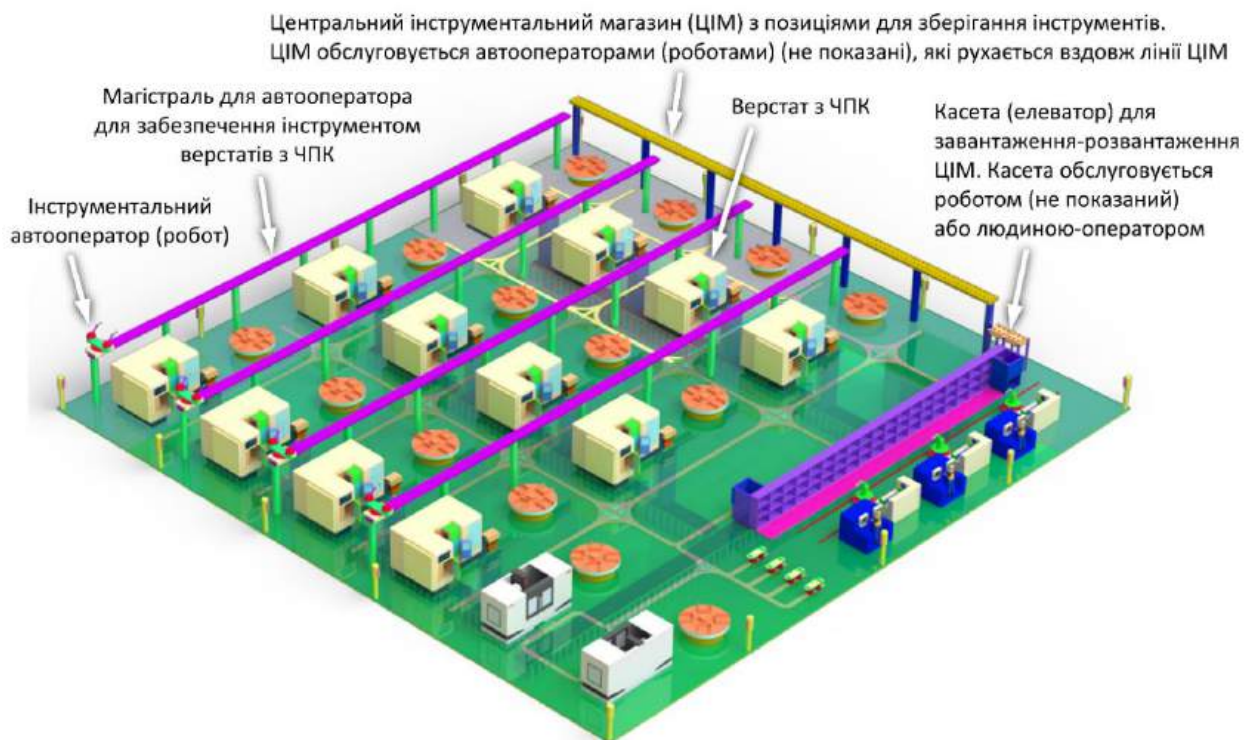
Загальний вигляд гнучкої виробничої системи механічної обробки з центральним інструментальним магазином (ЦІМ) для забезпечення верстатів з ЧПК інструментами
